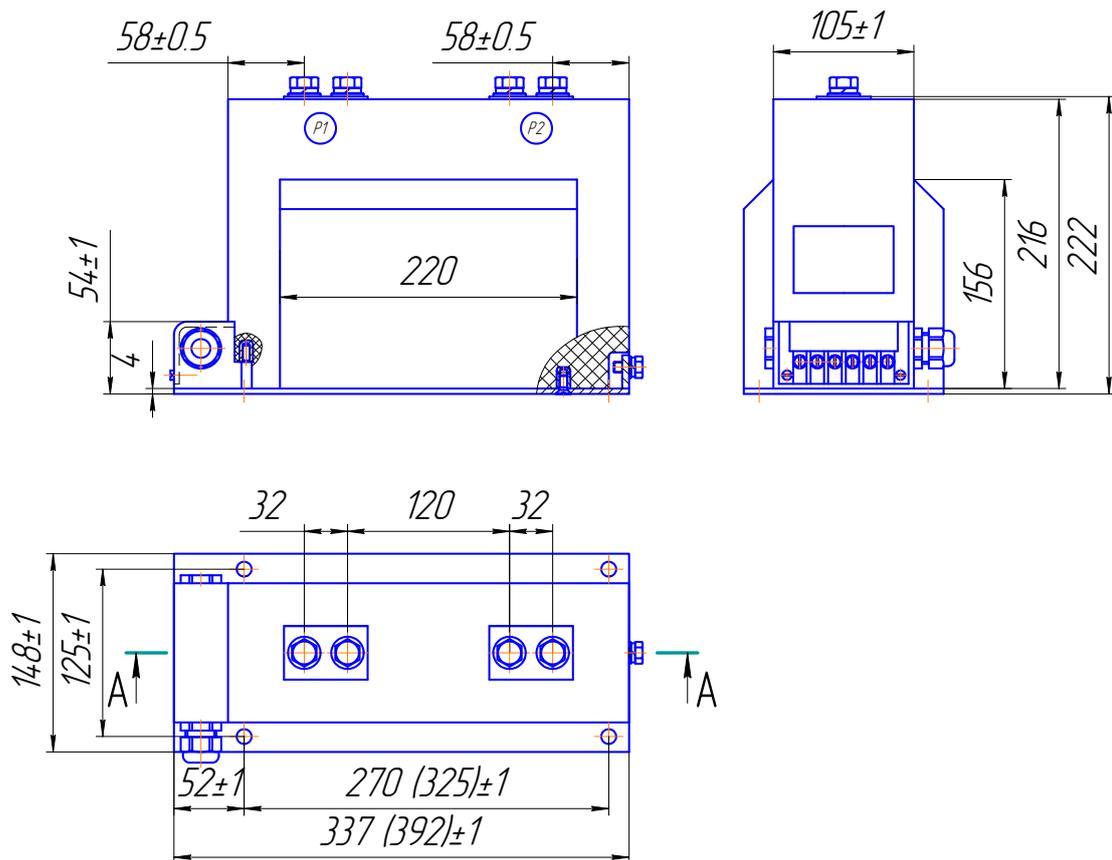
Общая компоновка, габаритные размеры трансформаторов тока ТОЛА.
